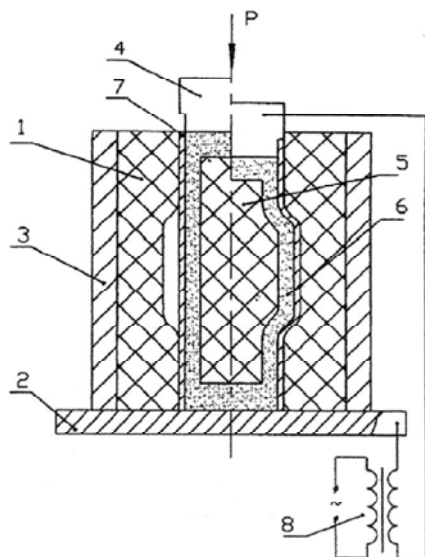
Схема устройства для раздачи труб с электроконтактным нагревом:
